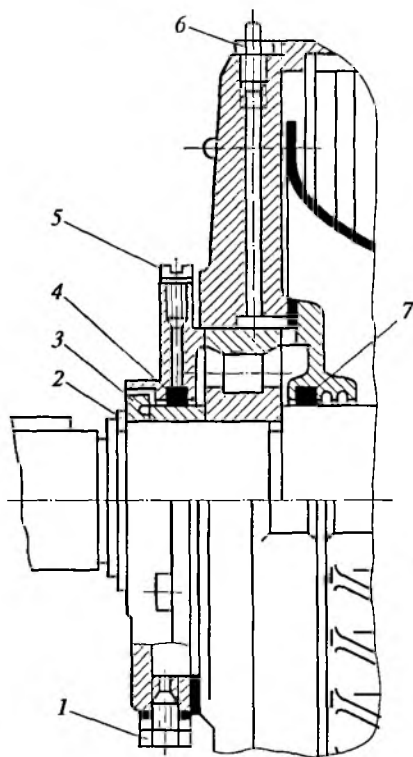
Подшипниковый узел с устройством для пополнения смазки:
